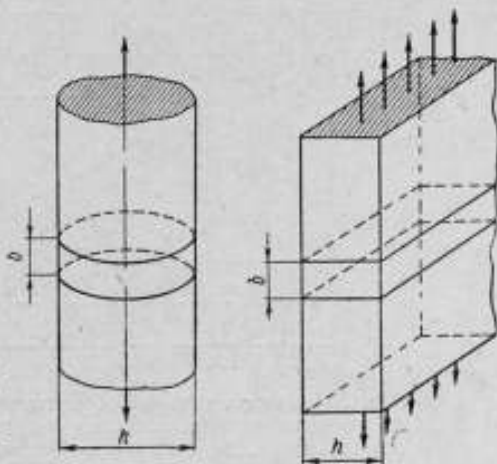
Схема сварного стыкового соединения с мягкой прослойкой.
